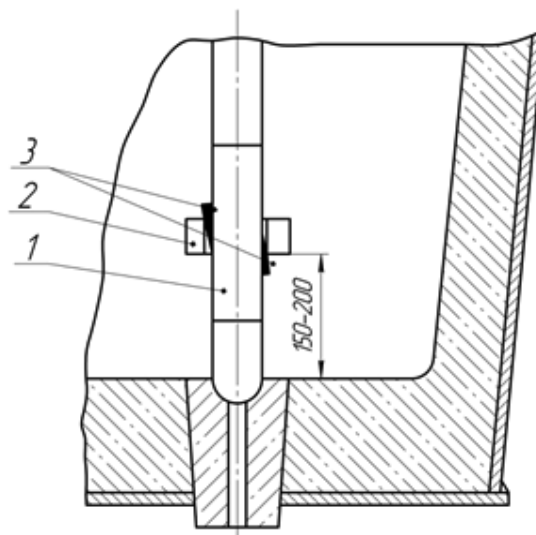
Установка алюминиевого кольца для раскисления стали в ковше: 1 – стопор; 2 – алюминиевое кольцо; 3 – клинья
